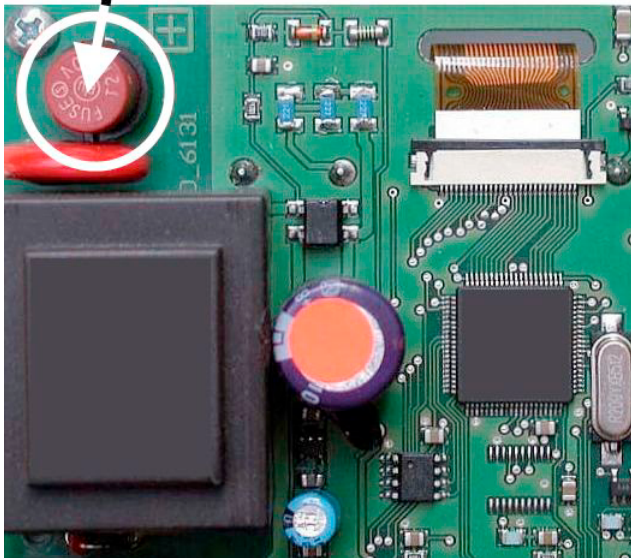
Positionnement du coupe-circuit dans le régulateur
